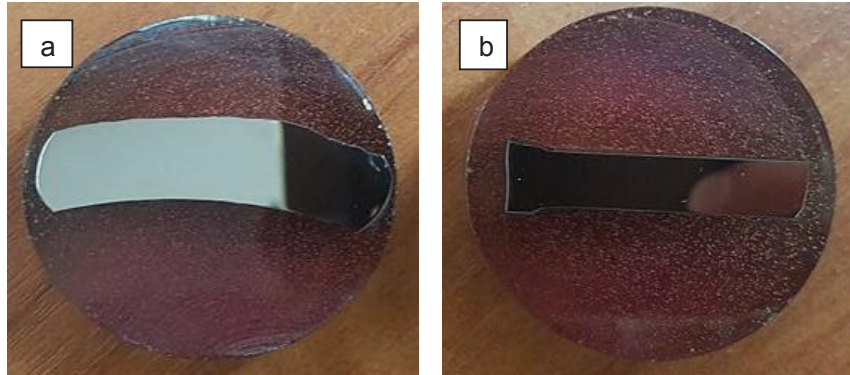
(a) Corte longitudinal a través de la soldadura, (b) Corte transversal.
